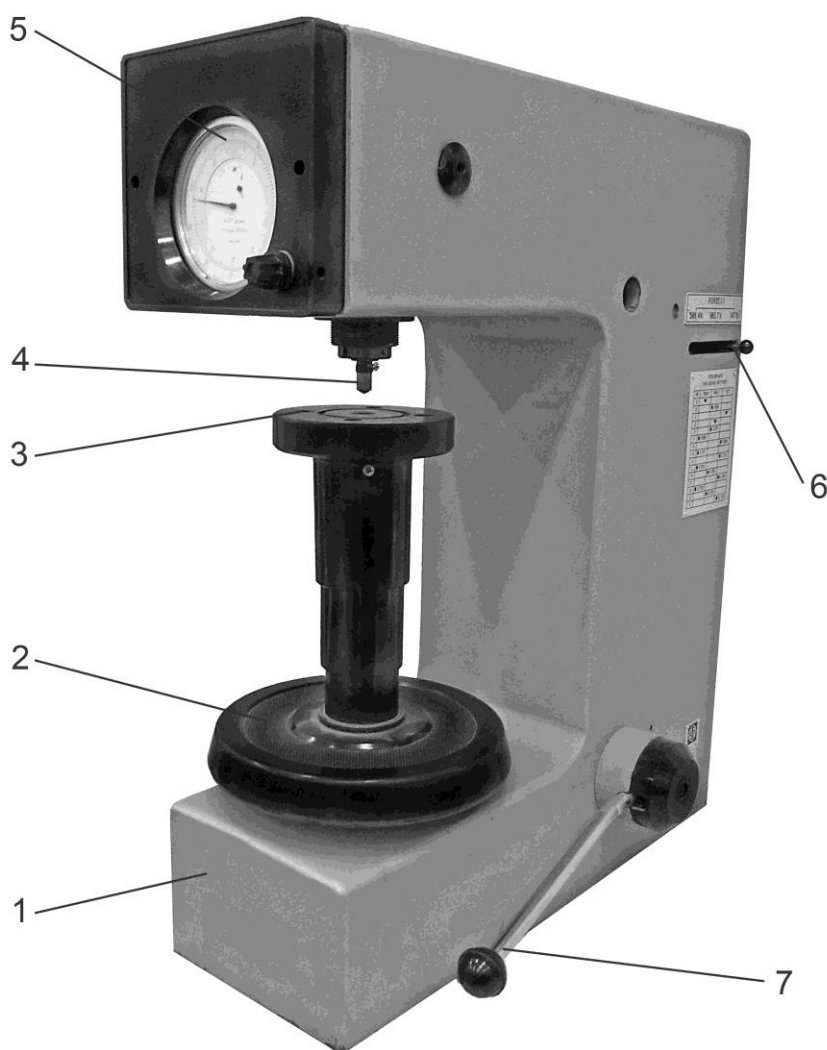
Внешний вид прибора типа TP 5006 для измерения твердости по Роквеллу:
